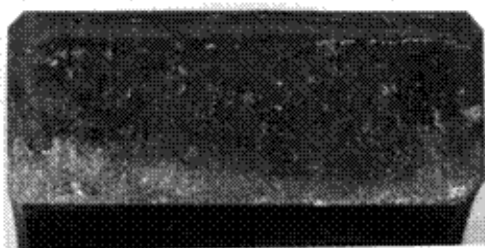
Strat carburat într-o rolă de pod rulant
